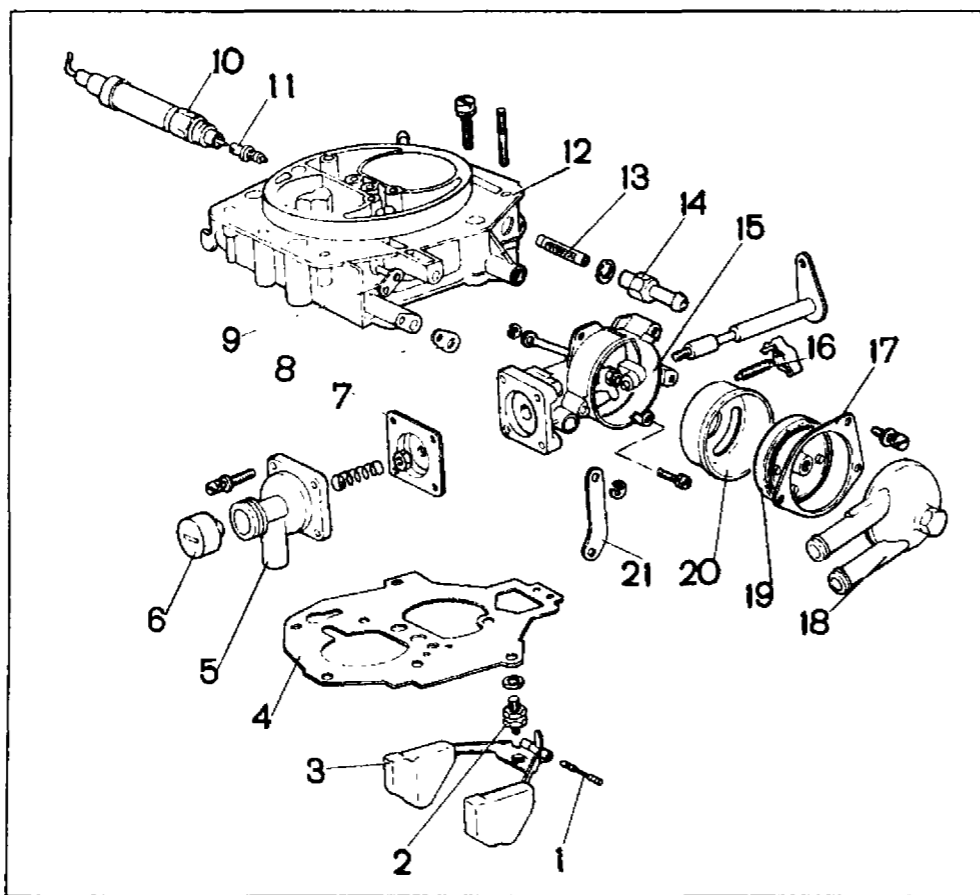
Детали крышки карбюратора: 1 — ось поплавка; 2 — игольчатый клапан; 3 — поплавок; 4 — прокладка крышки карбюратора; 5 — крышка пускового устройства в сборе; 6 — упор плунжера; 7 — диафрагма пускового устройства; 8 — прокладка; 9 — рычаг воздушной заслонки; 10 — актуатор системы холостого хода; 11 — топливный жиклер актуатора; 12 — крышка карбюратора; 13 — топливный фильтр; 14 — патрубок подачи топлива; 15 — корпус полуавтоматического пускового устройства в сборе с рычагами привода; 16 — регулировочный винт приоткрывания дроссельной заслонки первой камеры; 17 — хомут крепления корпуса биметаллической пружины; 18 — жидкостная камера; 19 — корпус с биметаллической пружиной в сборе; 20 — экран биметаллической пружины; 21 — тяга рычага приоткрывания дроссельной заслонки
